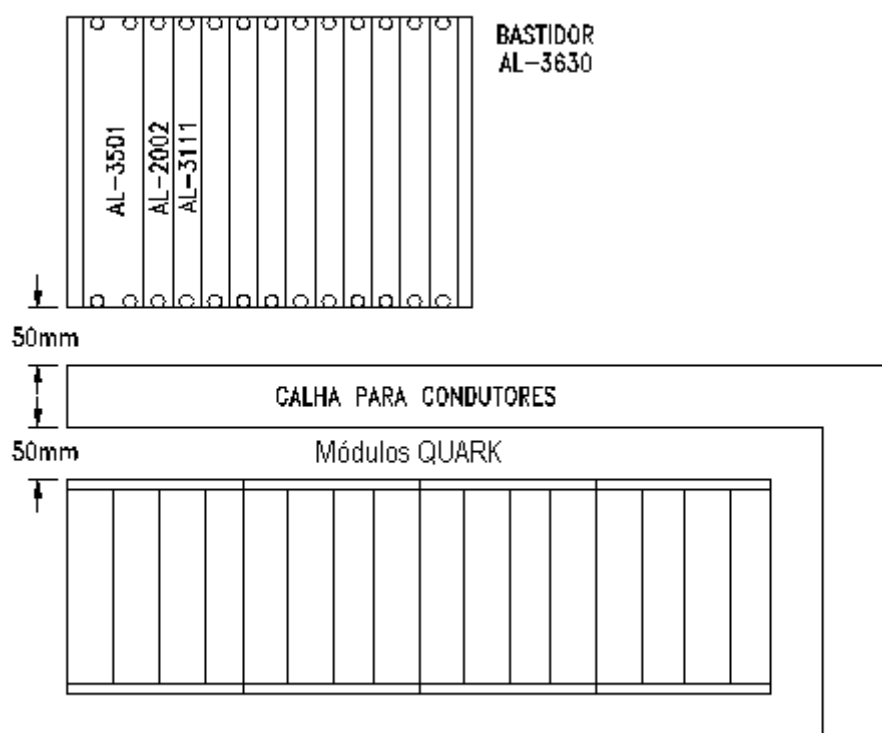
Painel de Montagem (dimensões em mm)
